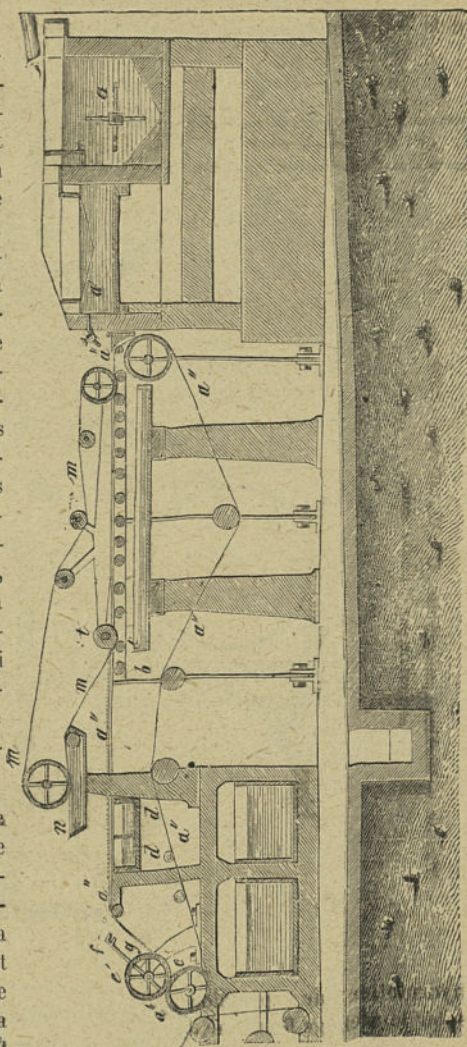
Machine à papier ; fabrication de la feuille continue.
